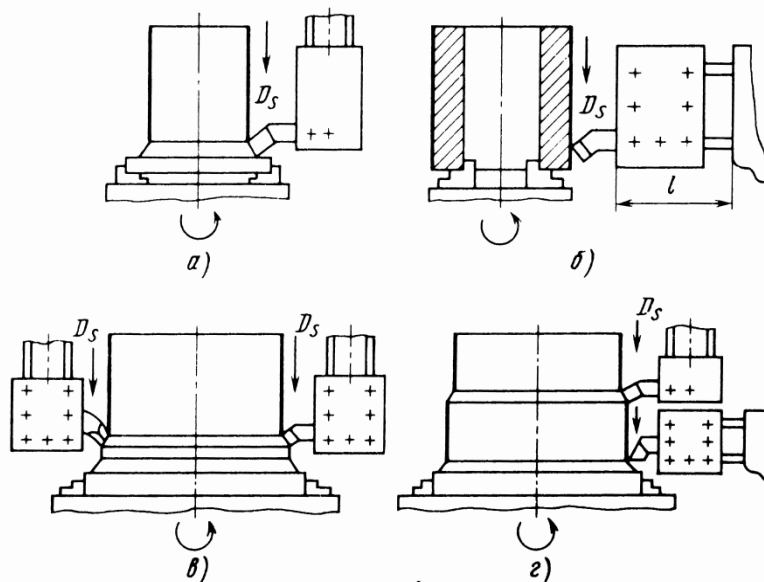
Схемы точения цилиндрических поверхностей на токарно-карусельных станках:
